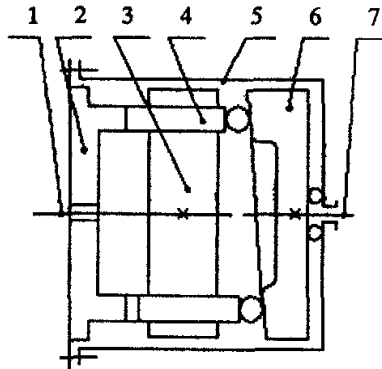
活齿端面谐波齿轮单边传动的结构示意图 (端面齿轮固定)
